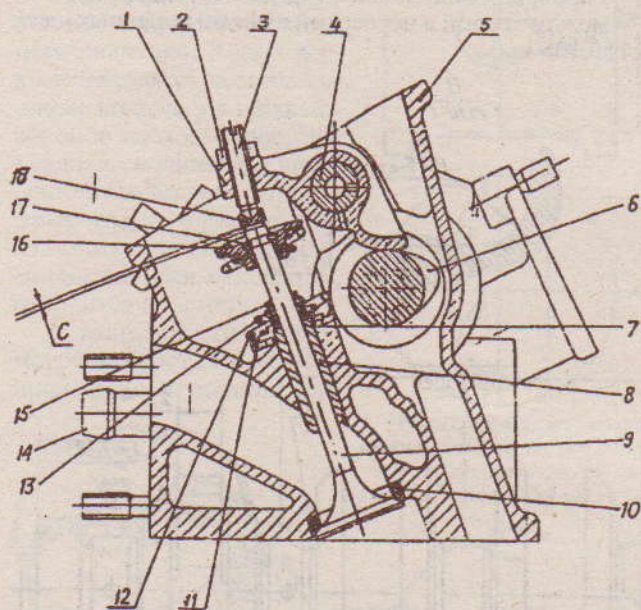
Головка цилиндров и схема регулировки зазоров в механизме привода клапана: 1 - коромысло; 2 - гайка; 3 - регулировочный винт коромысла клапана; 4 - ось коромысел; 5 - головка цилиндра; 6 - кулачок распределительного вала; 7 - кольцо стопорное; 8 - втулка направляющая; 9 - клапан; 10 - седло клапана; 11 - шайба опорная внутренней и наружной пружины; 12 и 13 - пружины наружная и внутренняя; 14 - патрубков; 15 - маслоотражательный колпачок клапана; 16 - тарелка пружины клапана; 17 - сухари тарелки клапана; 18 - наконечник регулировочного винта коромысла
